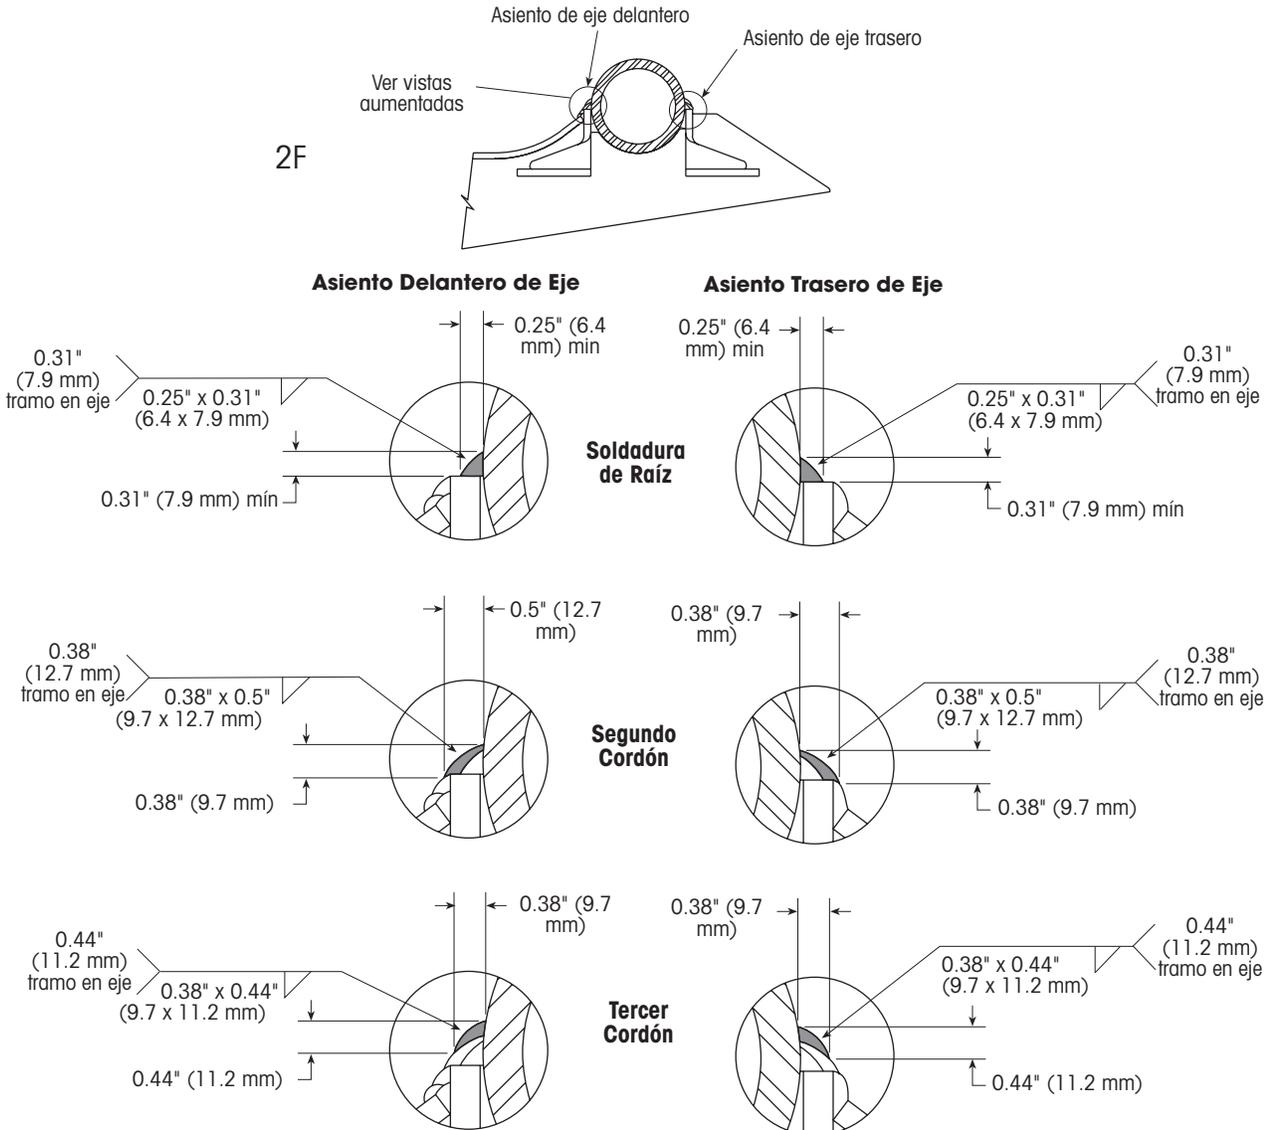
Cordón de soldadura — Todas las suspensiones Serie HT™
